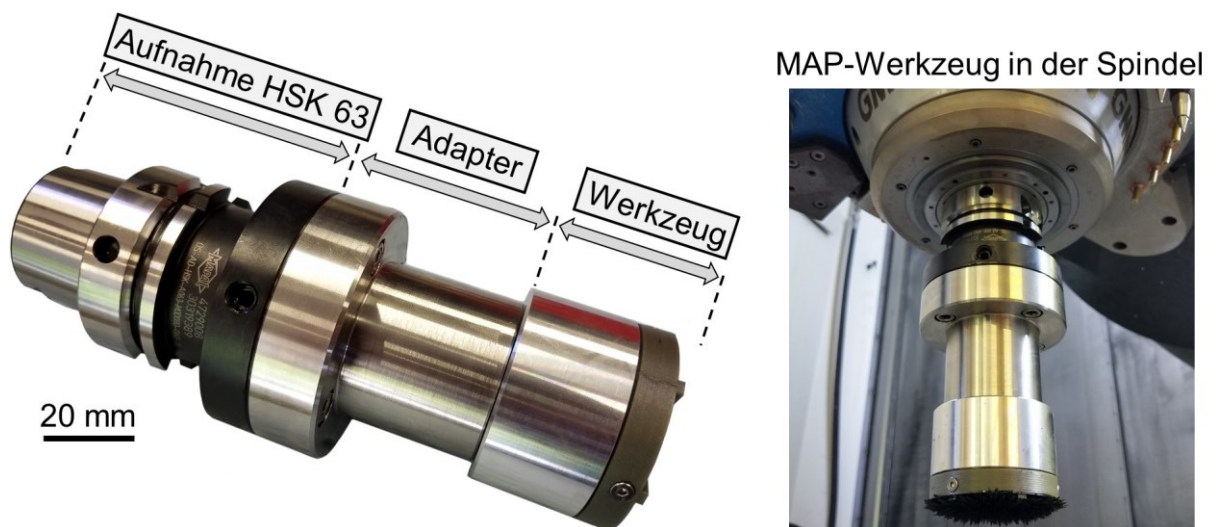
Aufnahme, paramagnetischer Adapter und MAP-Werkzeug
